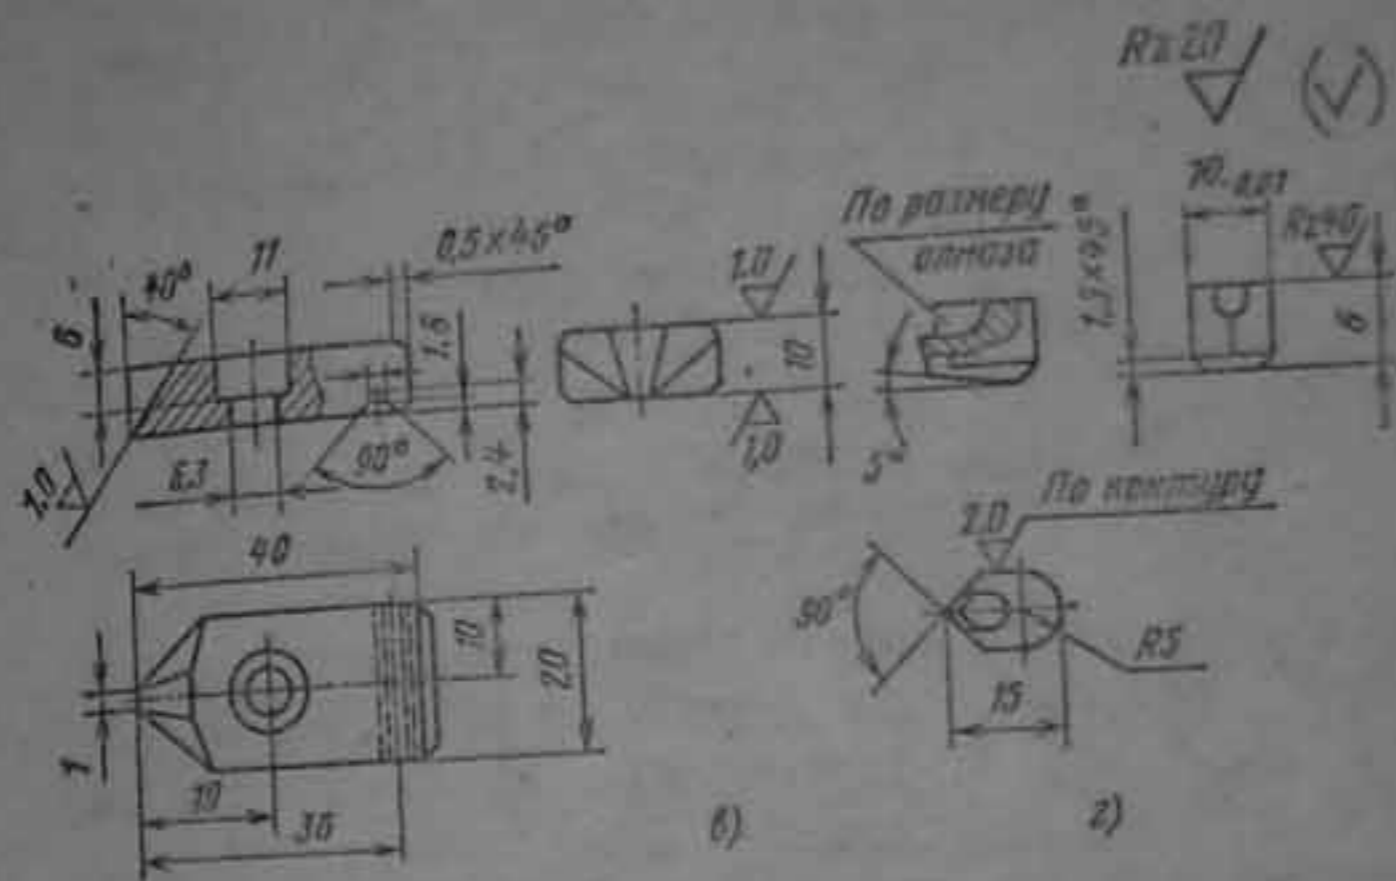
Чертеж токарного проходного сборного резца с механическим креплением алмаза:
